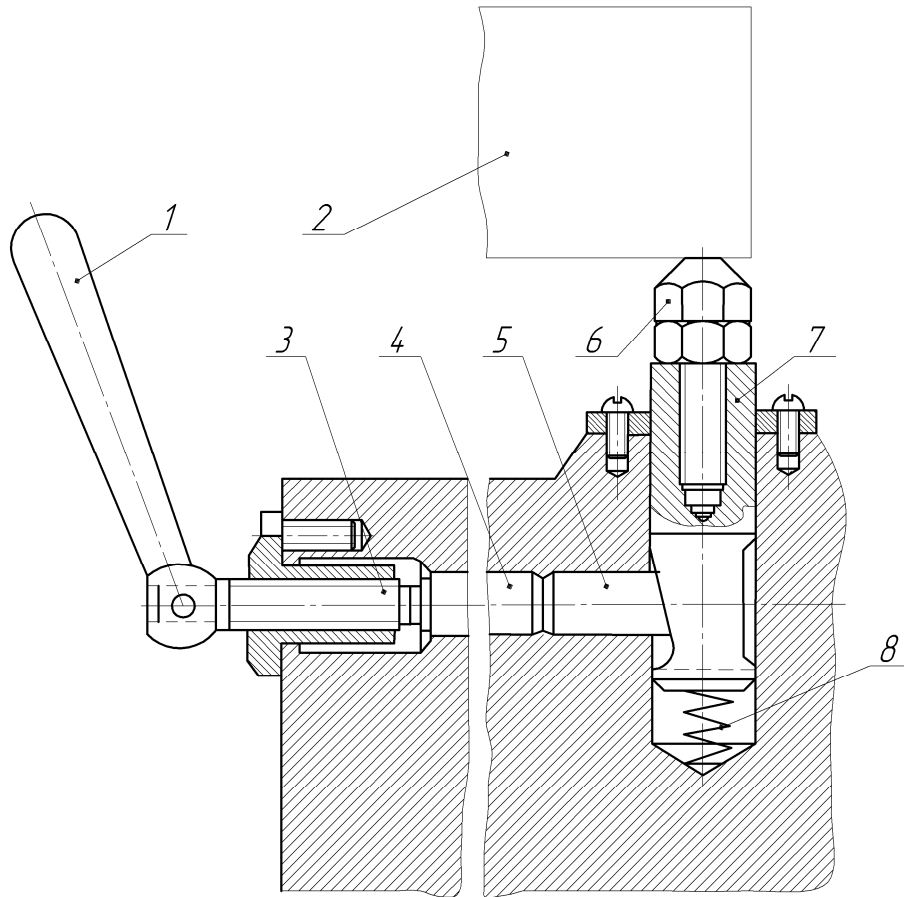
Будова самовстановлювальної опори: 1 – рукоятка; 2 – оброблювана деталь; 3, 6 – гвинти; 4, 5 – пальці; 7 – плунжер; 8 – пружина
